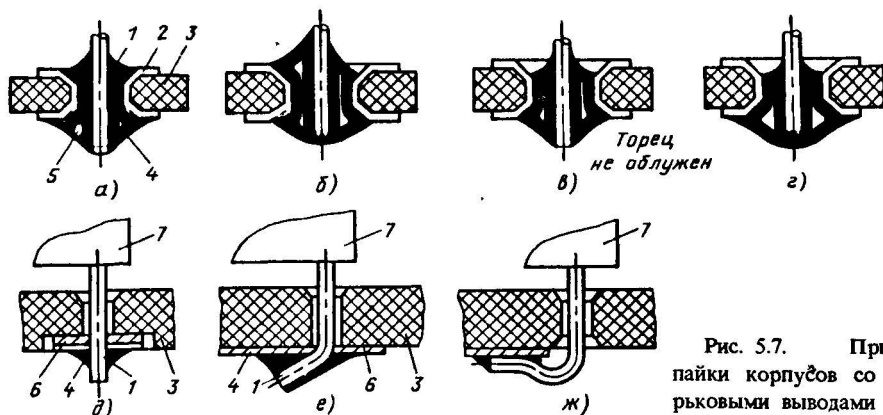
Примеры пайки корпусов со штырьковыми выводами
